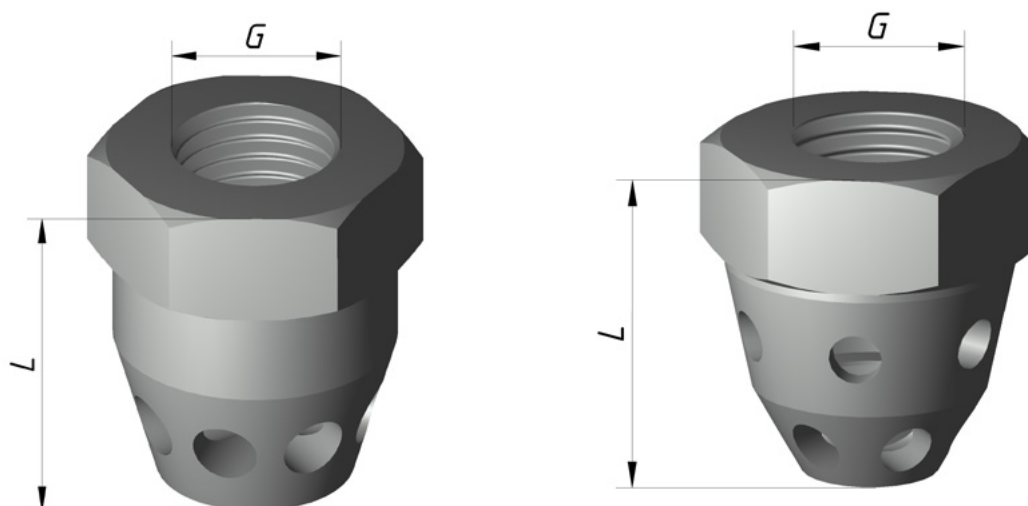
Насадки типа НВ-У (насадок выпускной универсальный)
